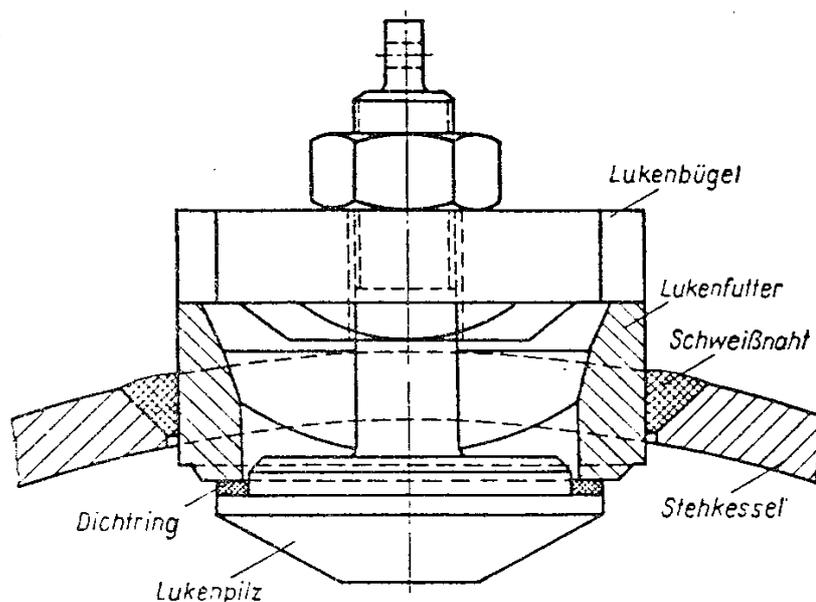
Kleine Waschluge mit eingeschweißtem Futter
